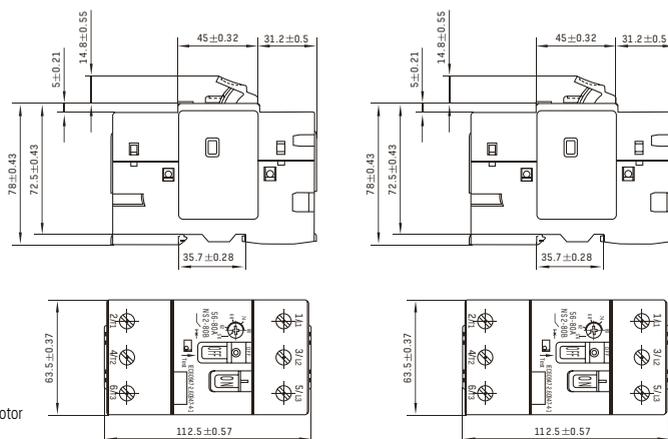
Dimensões gerais e de instalação do Disjuntor Motor
